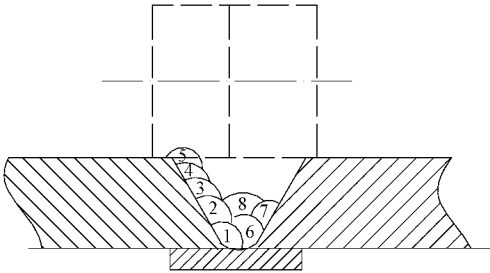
带背面垫板的对接焊缝的焊接示意图
